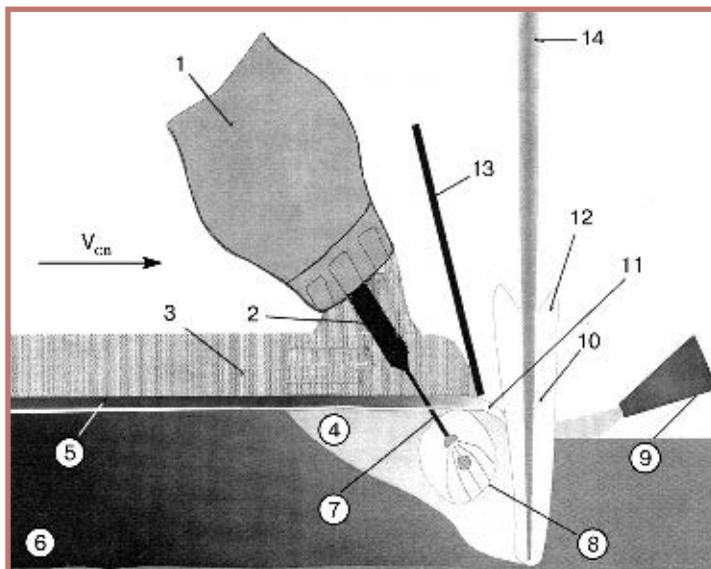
Схема гибридной лазерно-дуговой сварки под флюсом (LUPuS): 1 — бункер для флюса; 2 — контактный мундштук; 3 — флюс; 4 — ванна жидкого металла; 5 — шлаковая корка; 6 — металл сварного шва; 7 — сварочная проволока; 8 — зона горения дуги; 9 — сопло подачи гелия; 10 — парогазовый канал; 11 — расплавленный флюс; 12 — исходящие плазма и пары металла; 13 — разделительная пластина; 14 — лазерный пучок
